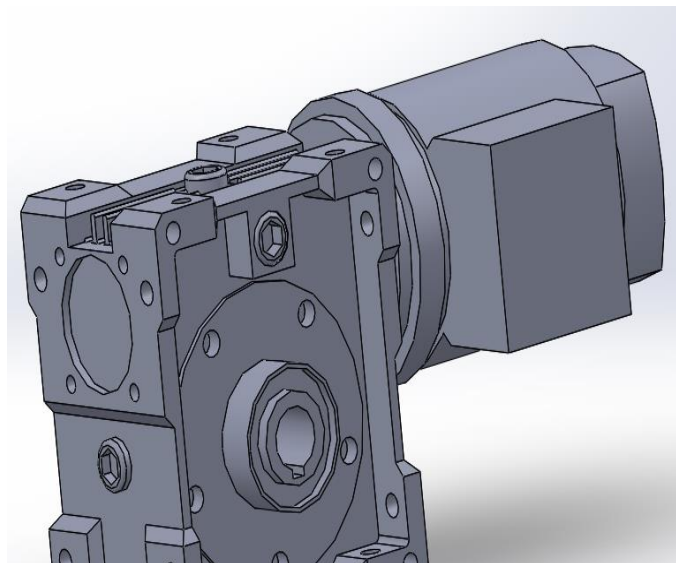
Motorreductor – desplazamiento de la máquina. Fuente: Autor
